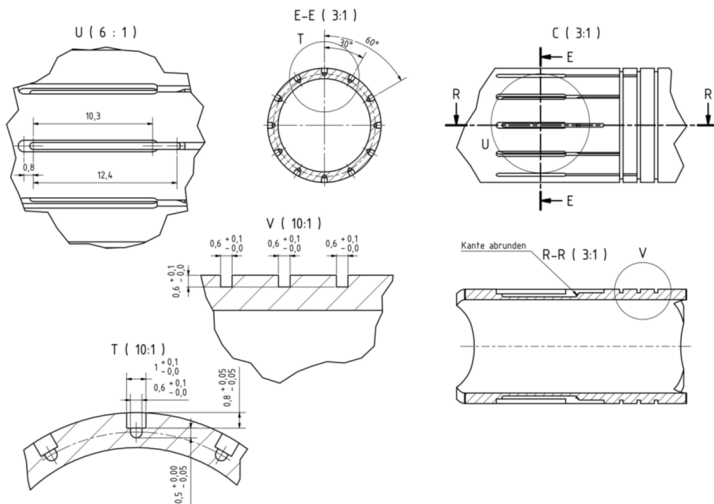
Technische Zeichnung des Messrohres aus Cu-DHP mit Nutbild und Positionierung der Thermoelemente.
